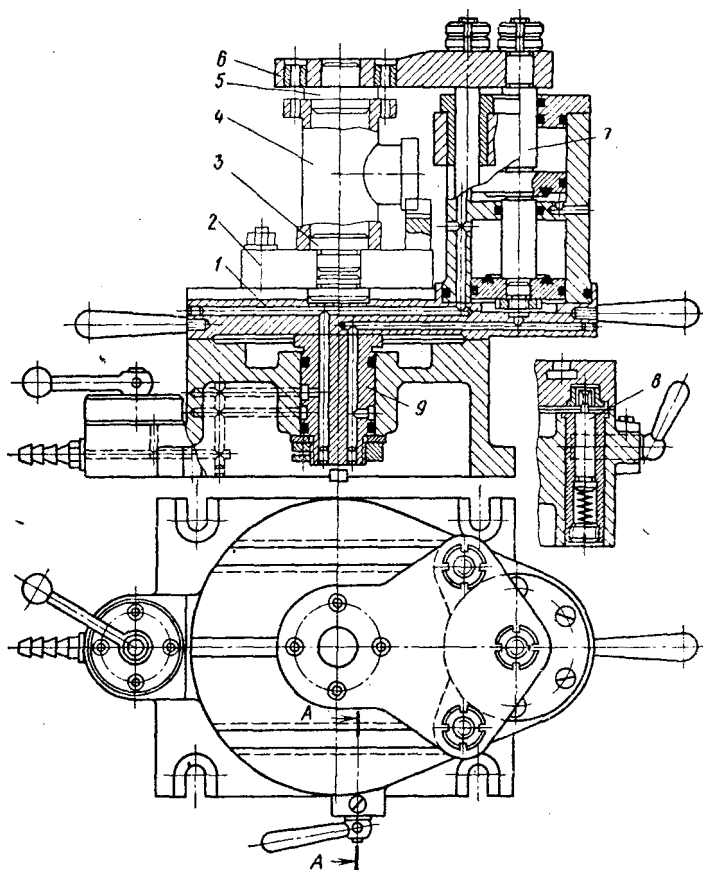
Групповое переналаживаемое приспособление для обработки отверстий в тройниках и полумуфтах
